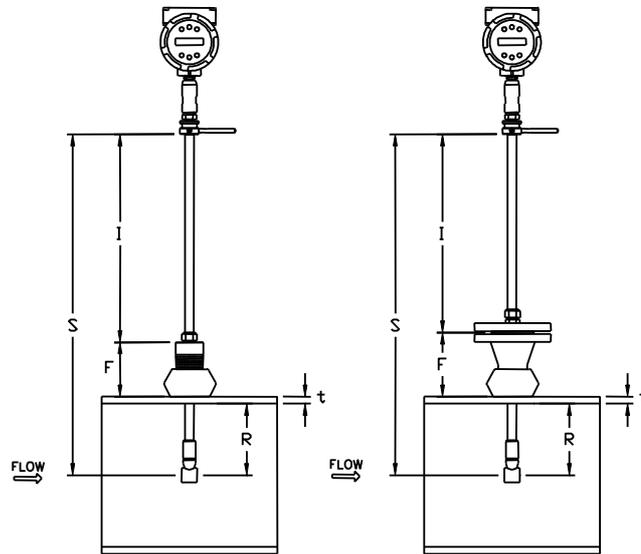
Berechnung der Eintauchtiefe (Schneidringverschraubung)"
